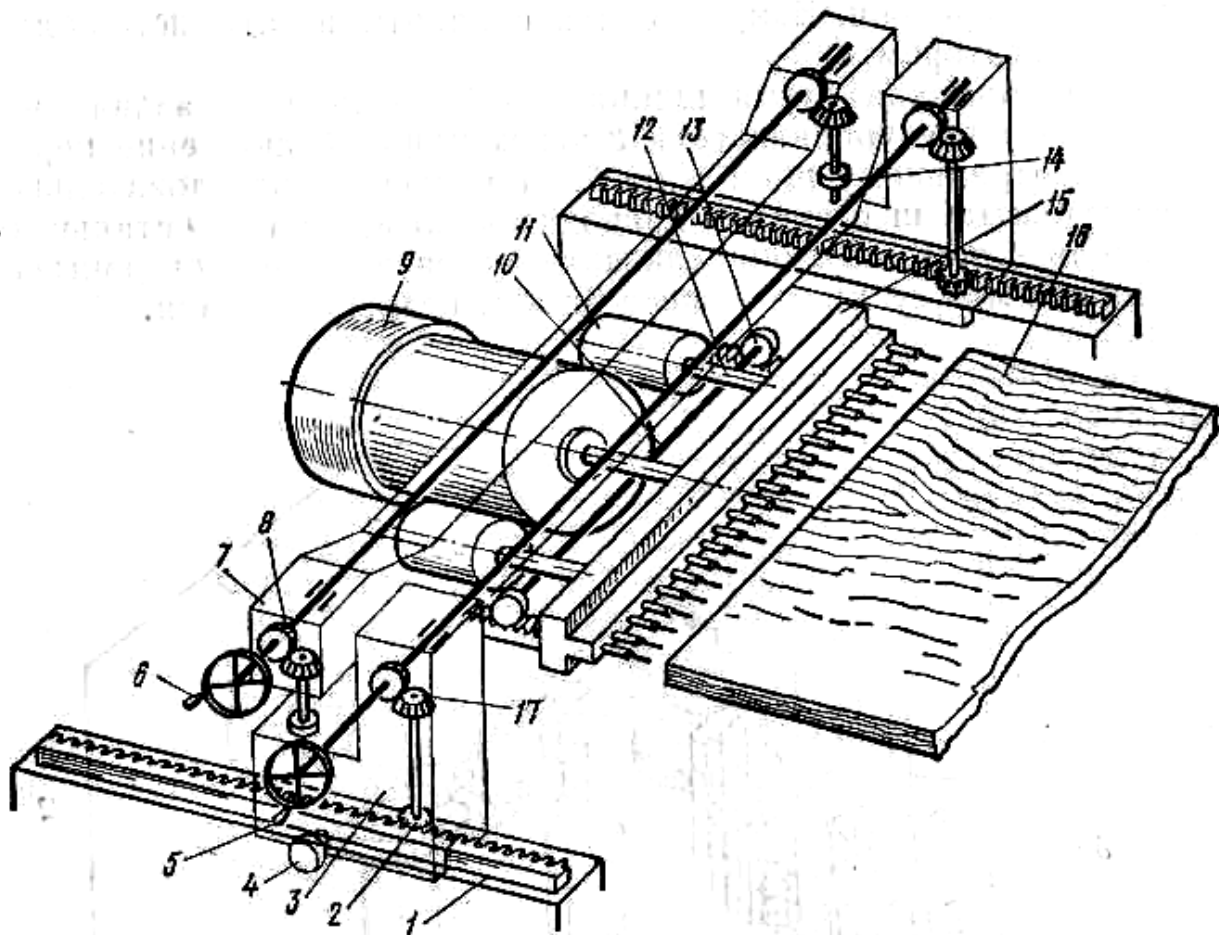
Сверлильный агрегат многошпиндельного станка:
